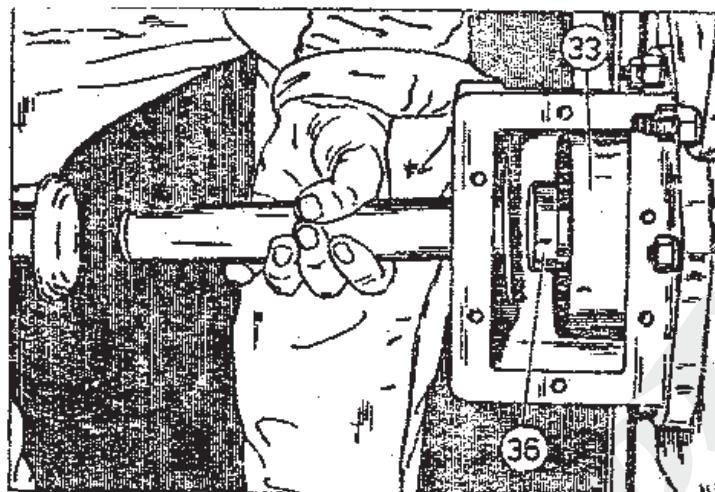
Вдавливание подшипника 6296 на валик с помощью втулки /32 - см. рис. 2-30/.
